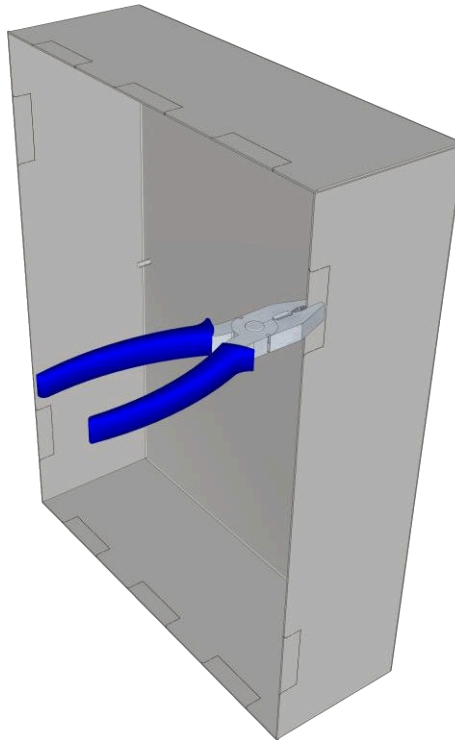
Metodo di rottura del rilievo per i fili di installazione.
